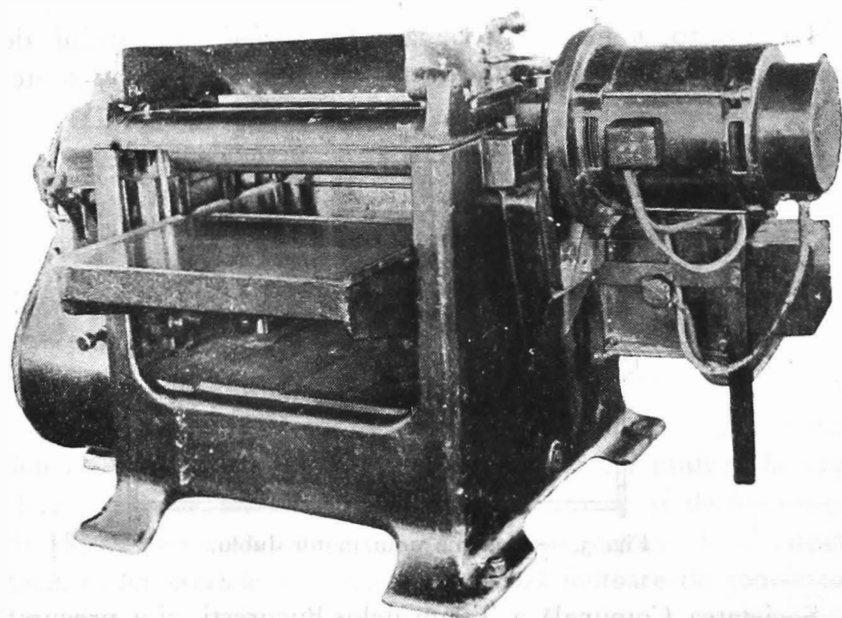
Mașină de grosime (Dicktenhohelmaschine) cu motor dublu.
